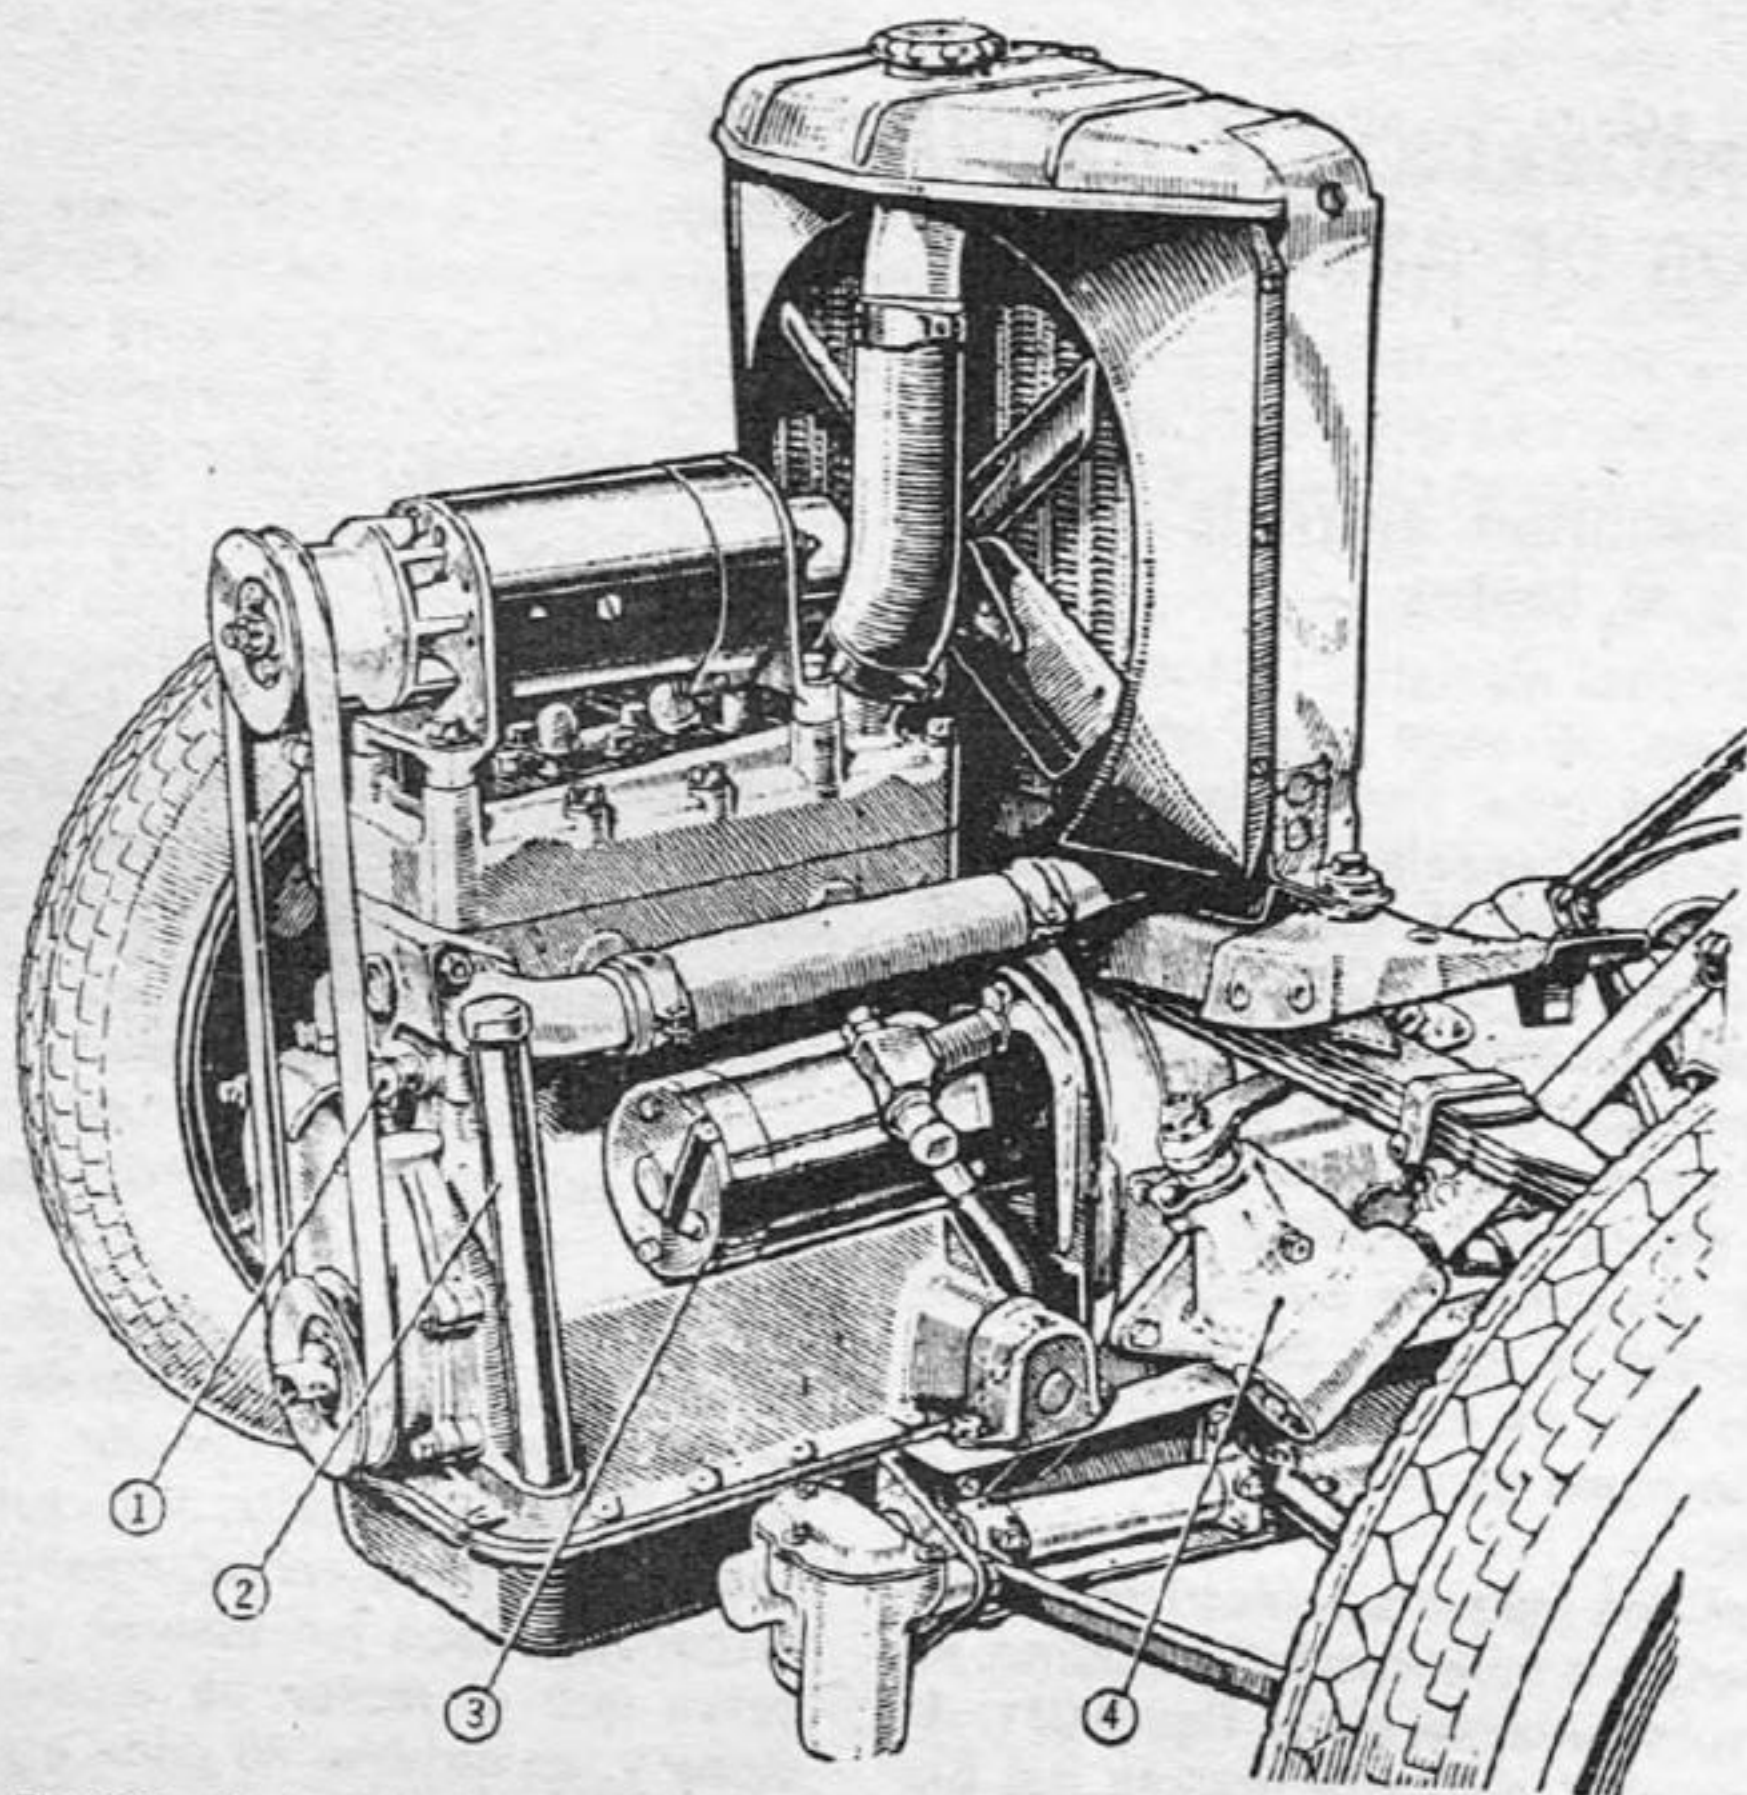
Parte delantera de un auto moderno representando la dinamo sobre el motor de explosión y el motorcito de arranque (3) debajo del tubo de refrigeración de los cilindros (cortesía de FIAT ARGENTINA S. A.).
